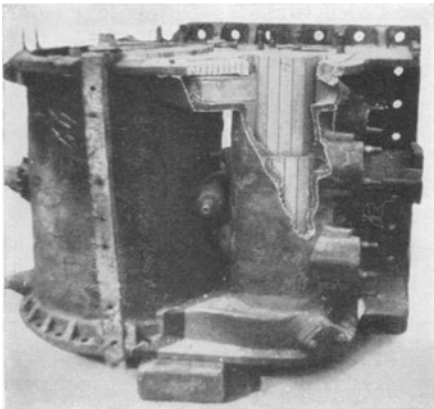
Lokomotivzylinder vor der Schweißung.
